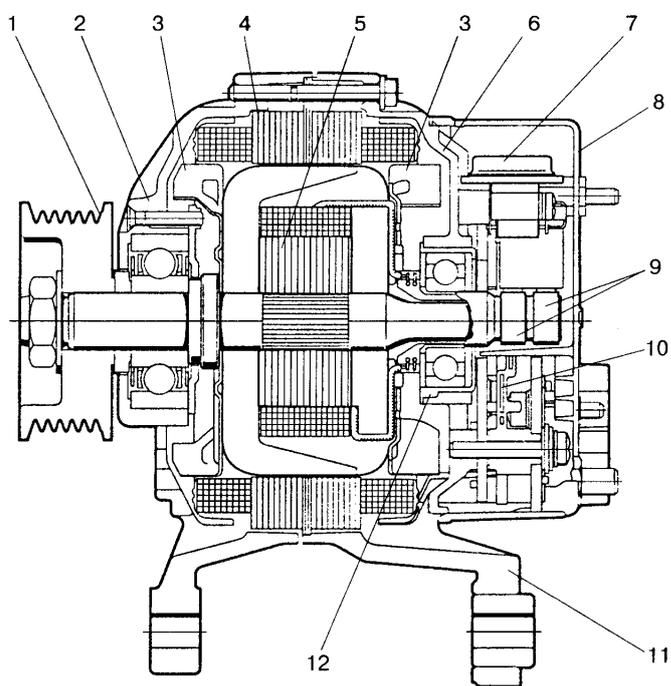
Устройство генераторов GC, KC и NC фирмы Bosch: 1 - шкив; 2, 6 - передняя и задняя крышки. 3 - вентиляторы; 4 - статор; 5 - стяжной винт; 7 - узел "щеткодержатель - регулятор напряжения"; 8 - защитный кожух; 9 - контактные кольца; 10 - выпрямительный блок; 11 - крепежная лапа; 12 -
